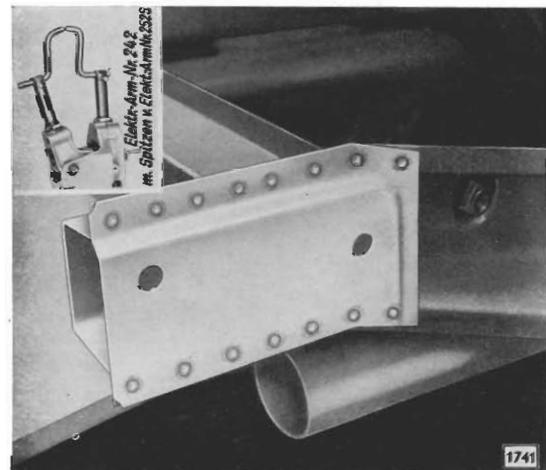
Schließblech an linken Längsträger zangenpunktschweißend – an rechten Längsträger Schließblech in gleicher Weise punktschweißen
